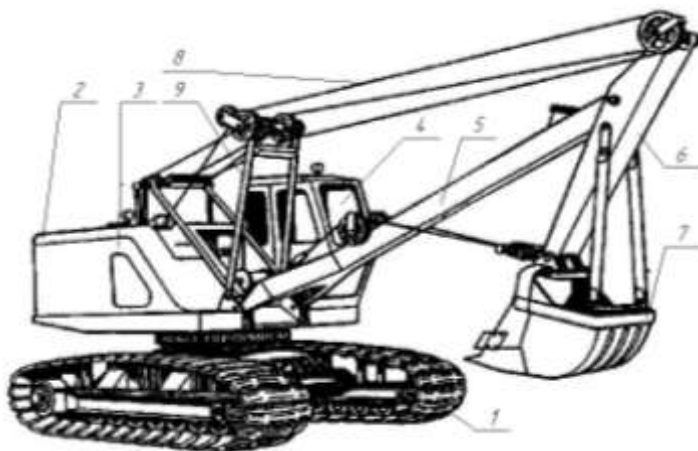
Экскаватор ЭО-3211Г с рабочим оборудованием обратная лопата: 1 – ходовое оборудование; 2 – поворотная платформа; 3 – двигатель; 4 – кабина; 5 – стрела; 6 – рукоять; 7 – ковш; 8 – система канатного управления; 9 – стойка передняя
